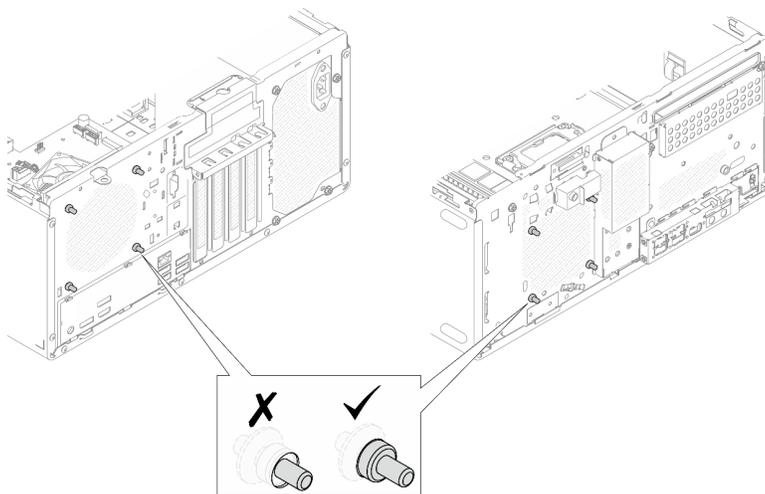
Instalação das montagens de borracha do ventilador frontal e traseiro
